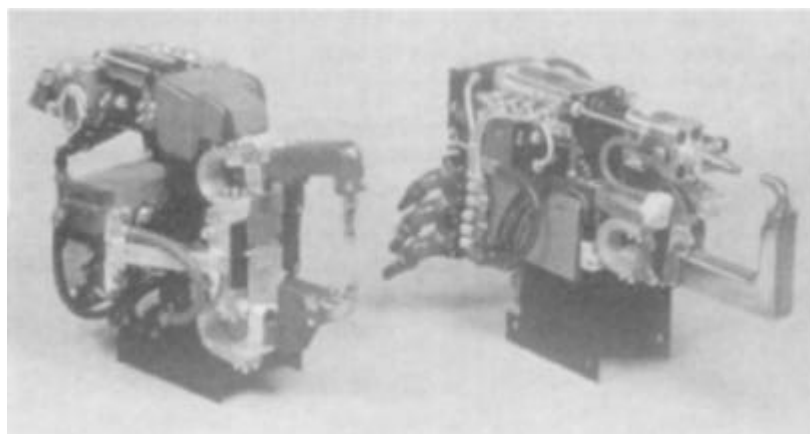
Pinzas de soldadura con transformador incorporado.
